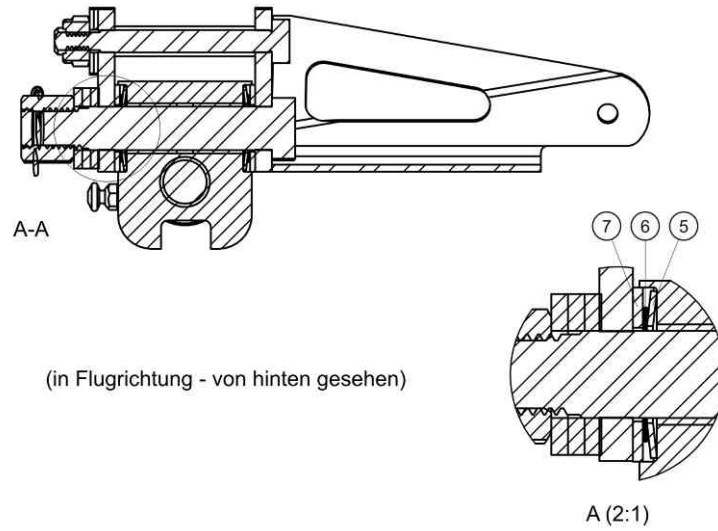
Messung der Reibkraft Rotorsteuerung
